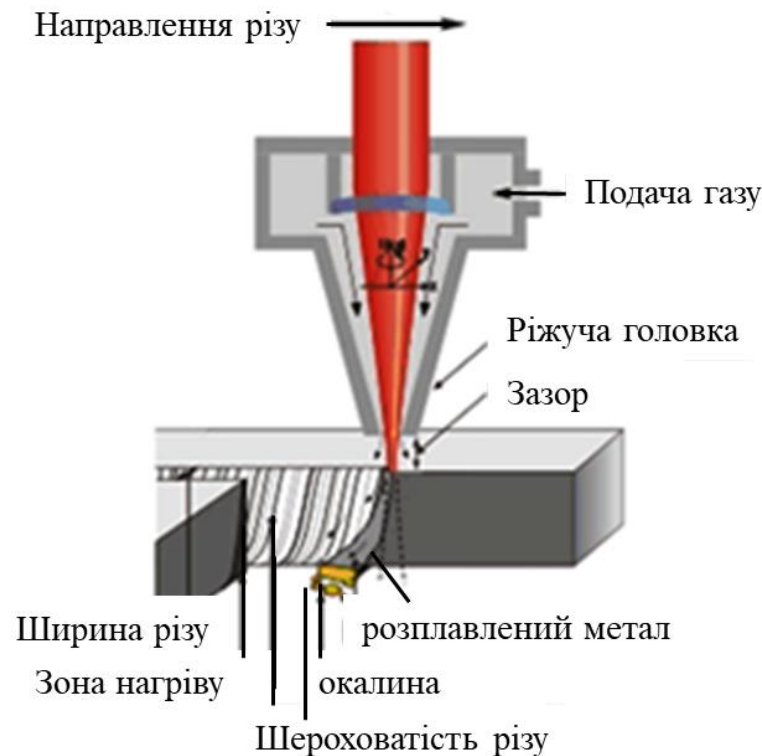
Схема газолазерного різання листових матеріалів
